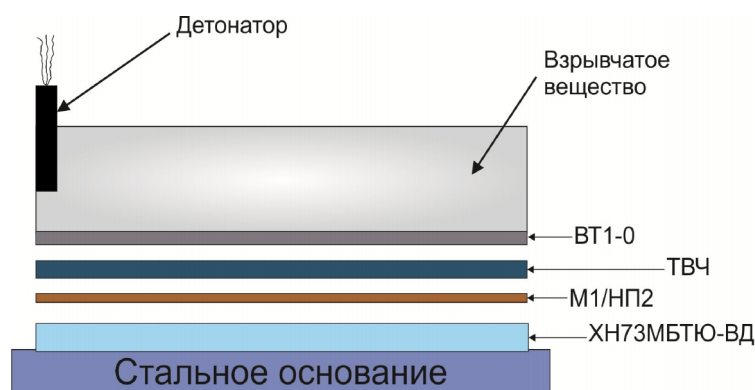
Схема сварки взрывом четырехслойных композитов
